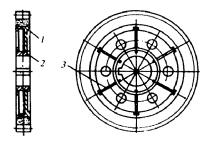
Зубчатый шевер для работы с окружным нагружением на станках с синхронным приводом инструмента и детали:
